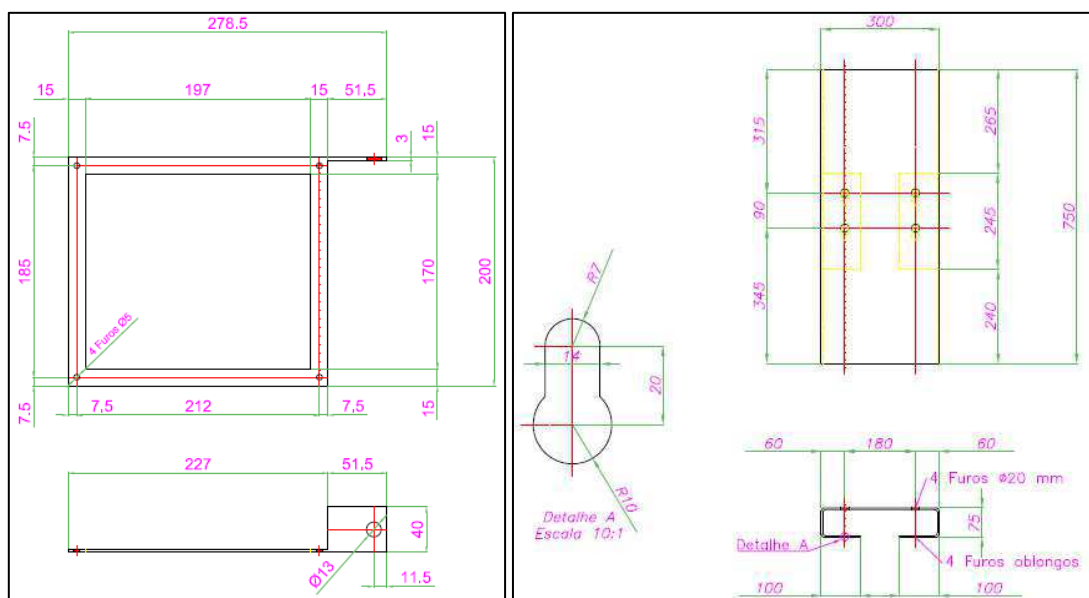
Desenho técnico do suporte para o controlador *Roland*.
